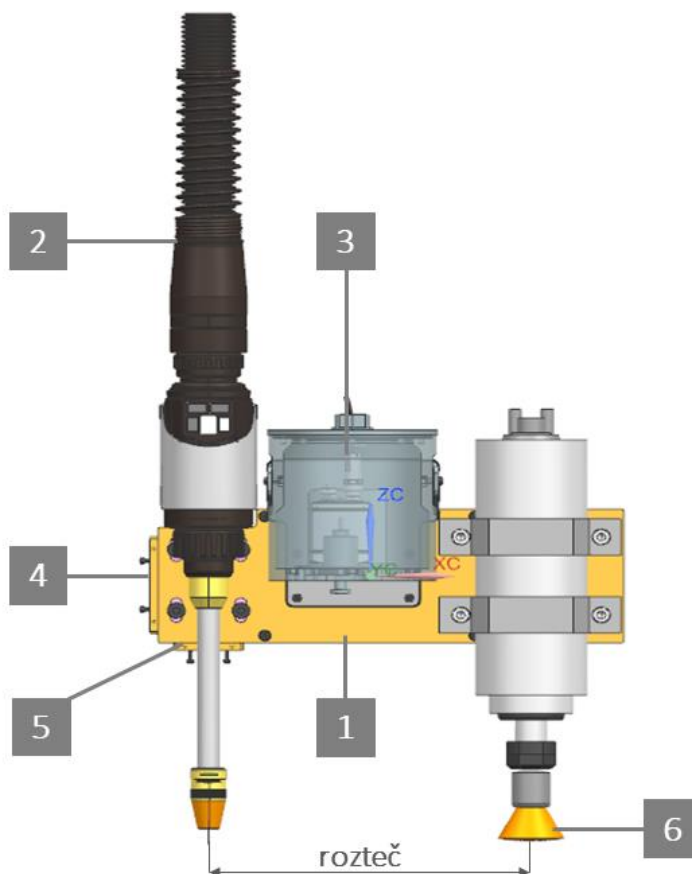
Porovnání konstrukce osy Z s původním provedením a upravenou konstrukcí
